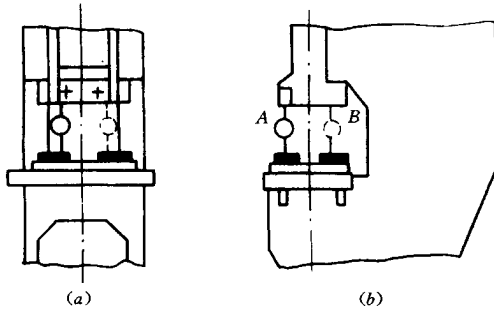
检验滑块下平面对工作台上平面的平行度
